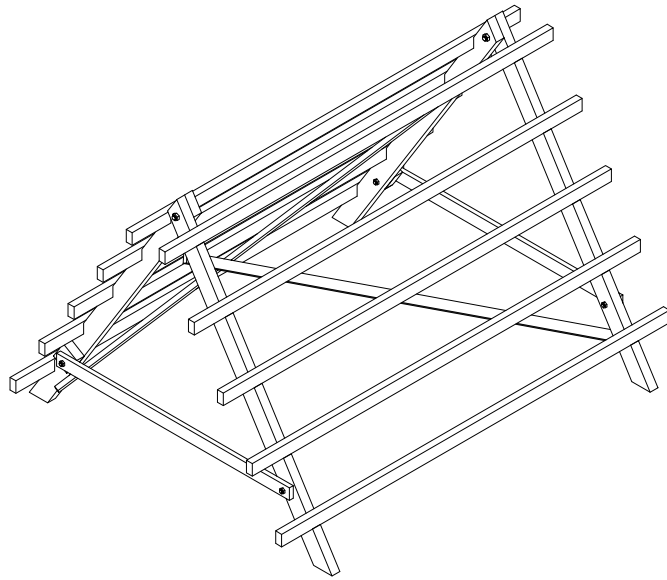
Stinghii de odihnă dispuse în formă de "A"(dimensiuni în mm)
